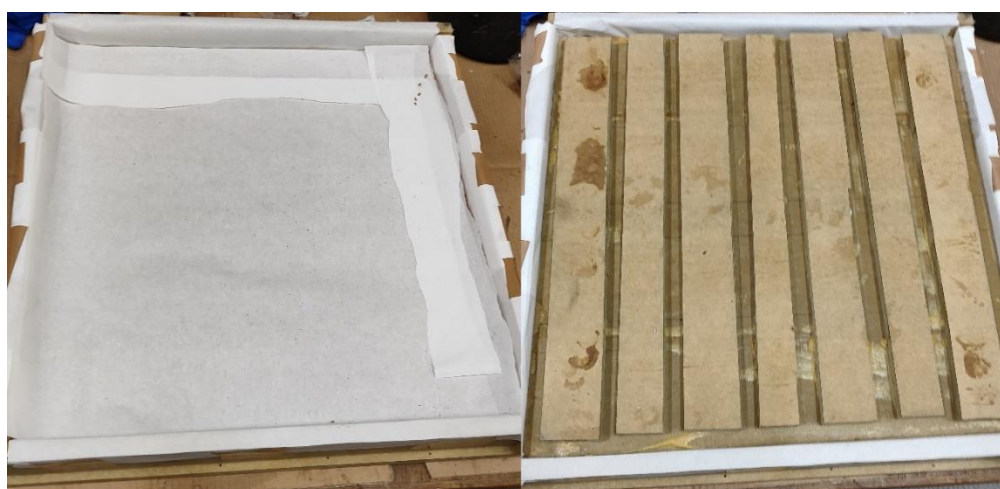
Revestimento superior de papel vegetal e molde fechado.
